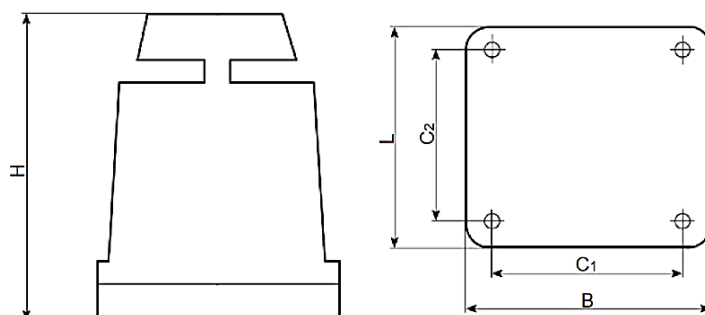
Габаритные и установочные размеры пакетных выключателей ПВ. Исполнение в карболитовом корпусе. Степень защиты IP30. Способ крепления - основанием корпуса.
